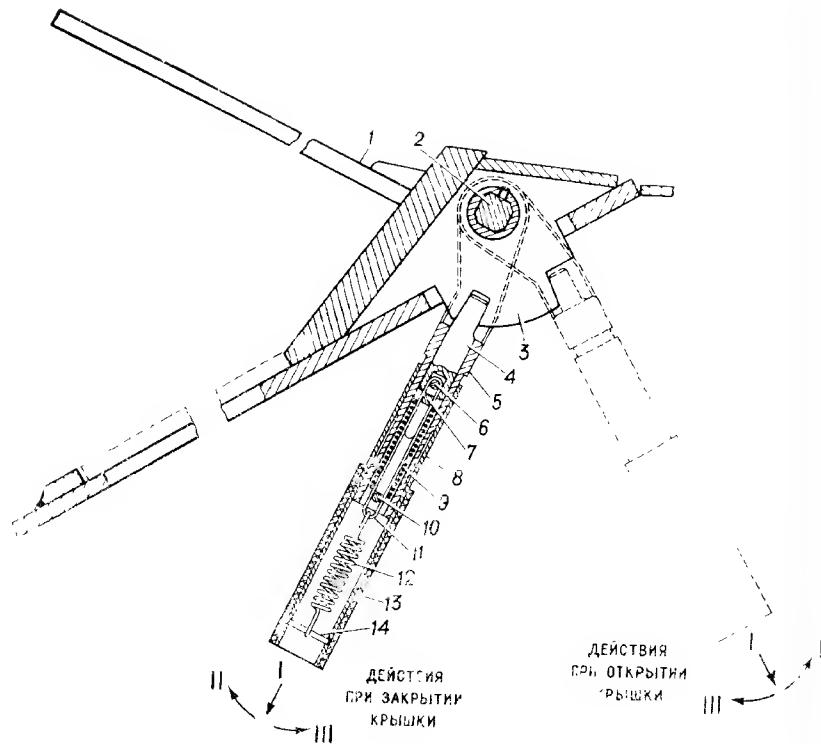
Рукоятка крышки смотрового люка командира (механика-водителя):
